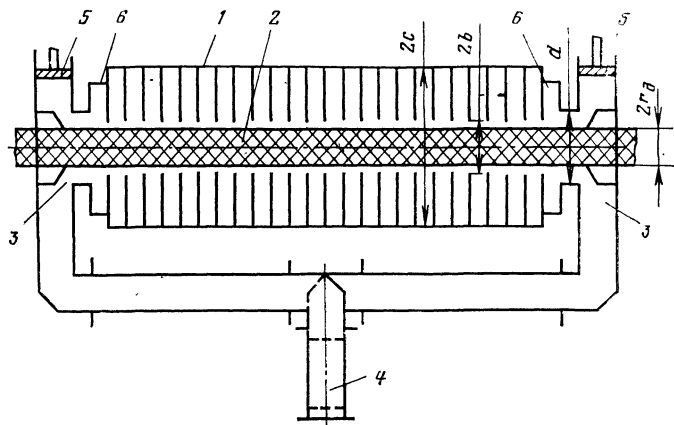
Схема СВЧ нагревателя для термообработки сосисочного фарша:
